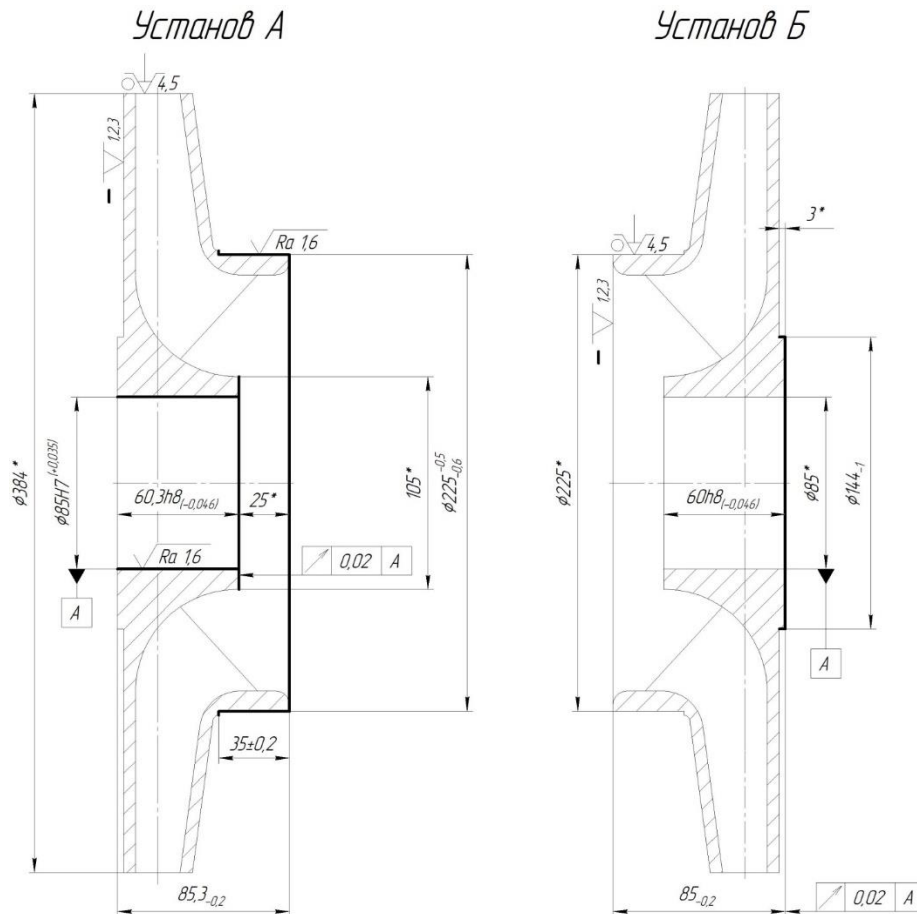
Схема установки заготовки на токарній операції (варіант 2)
